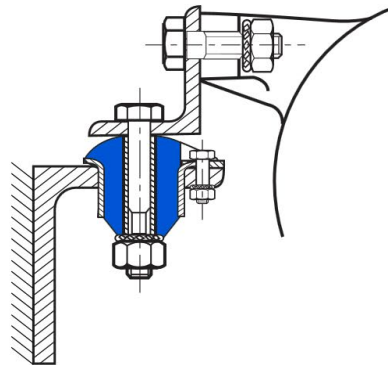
Montaje entre pie de la maquina y chasis metálico.
